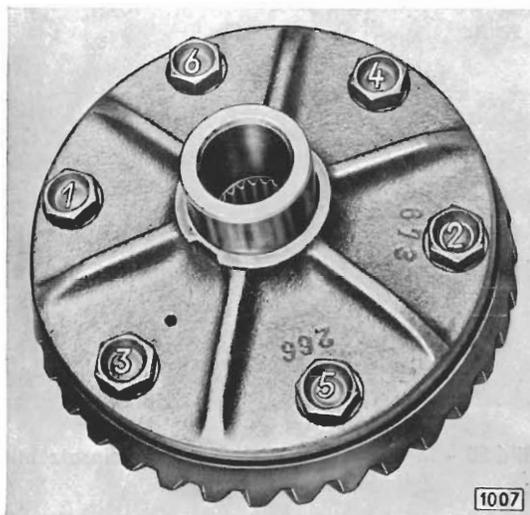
Reihenfolge für das Anziehen der Sechskant- bzw. Zwölfkant-Schaftschrauben des Tellerrades an das Ausgleichgehäuse
